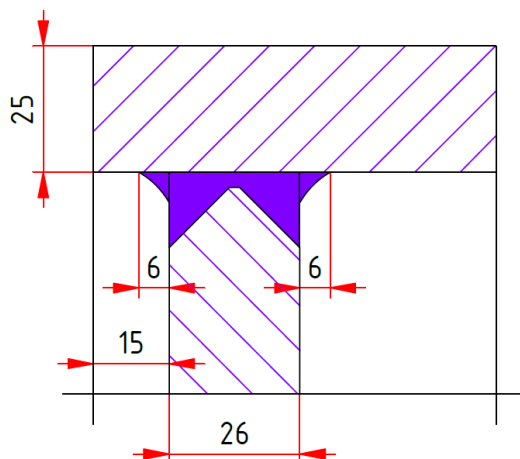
Detalj zavora cijevi priključka za cilindrični plašt
